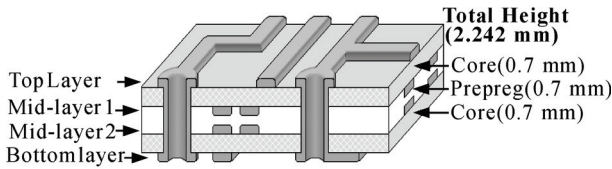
低功耗 Zigbee 遥控器 PCB 叠层结构
